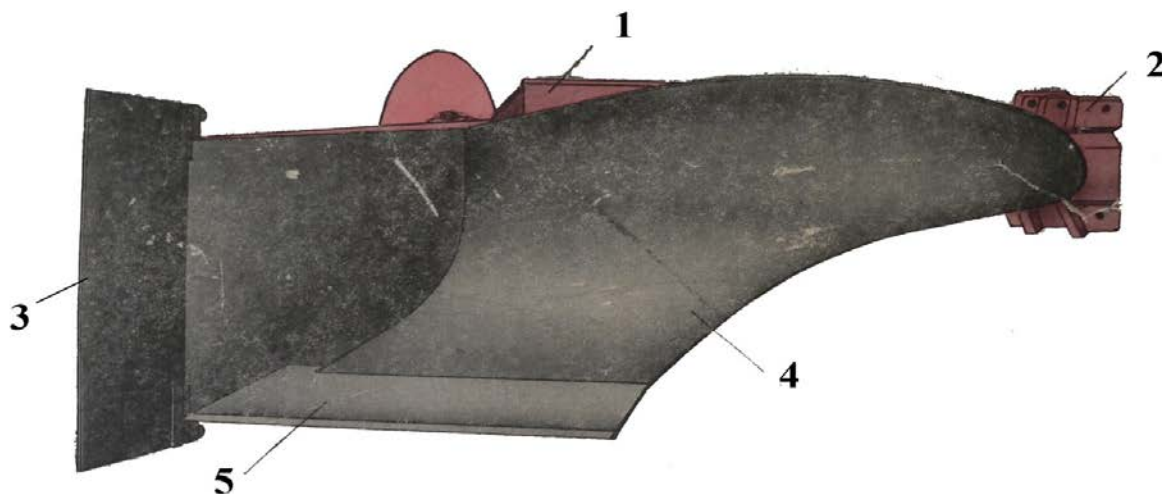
Корпус плуга ПЛП-135: 1 – рама, 2 – навесное устройство, 3 – нож-колуно, 4 – отвал, 5 – лемех
